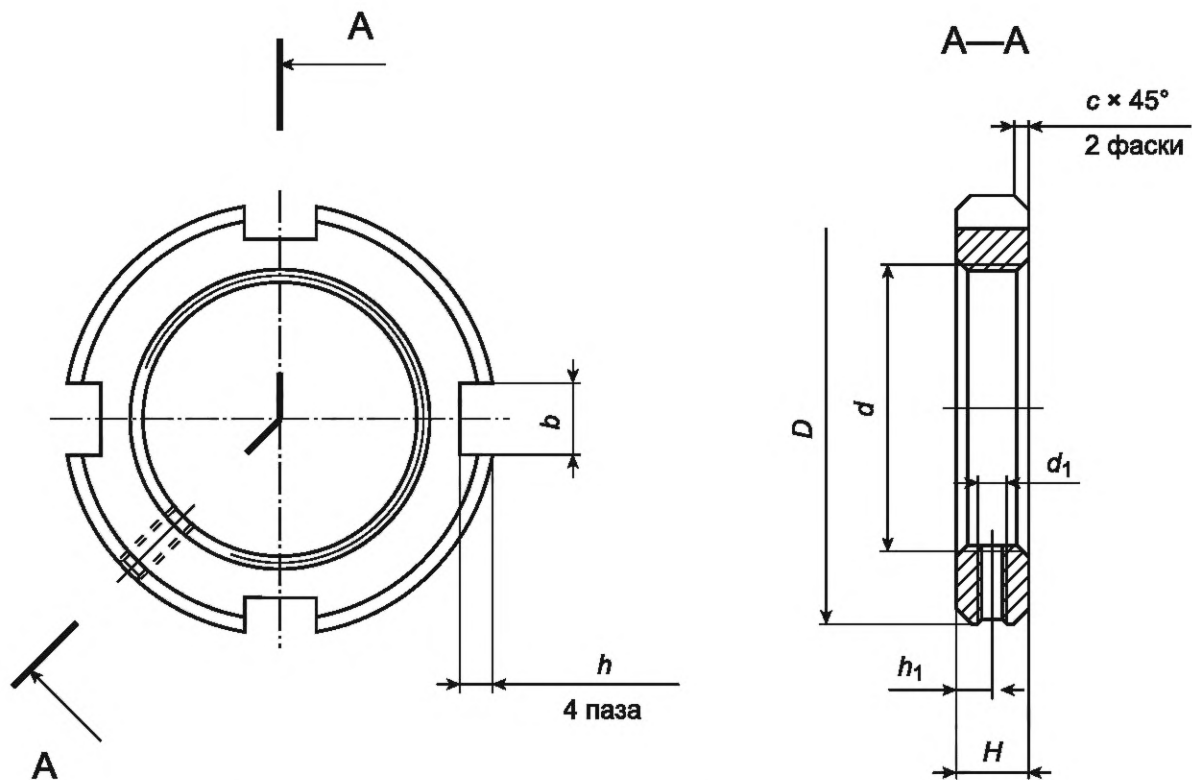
Конструкция шлицевых круглых гаек с отверстием для стопора
